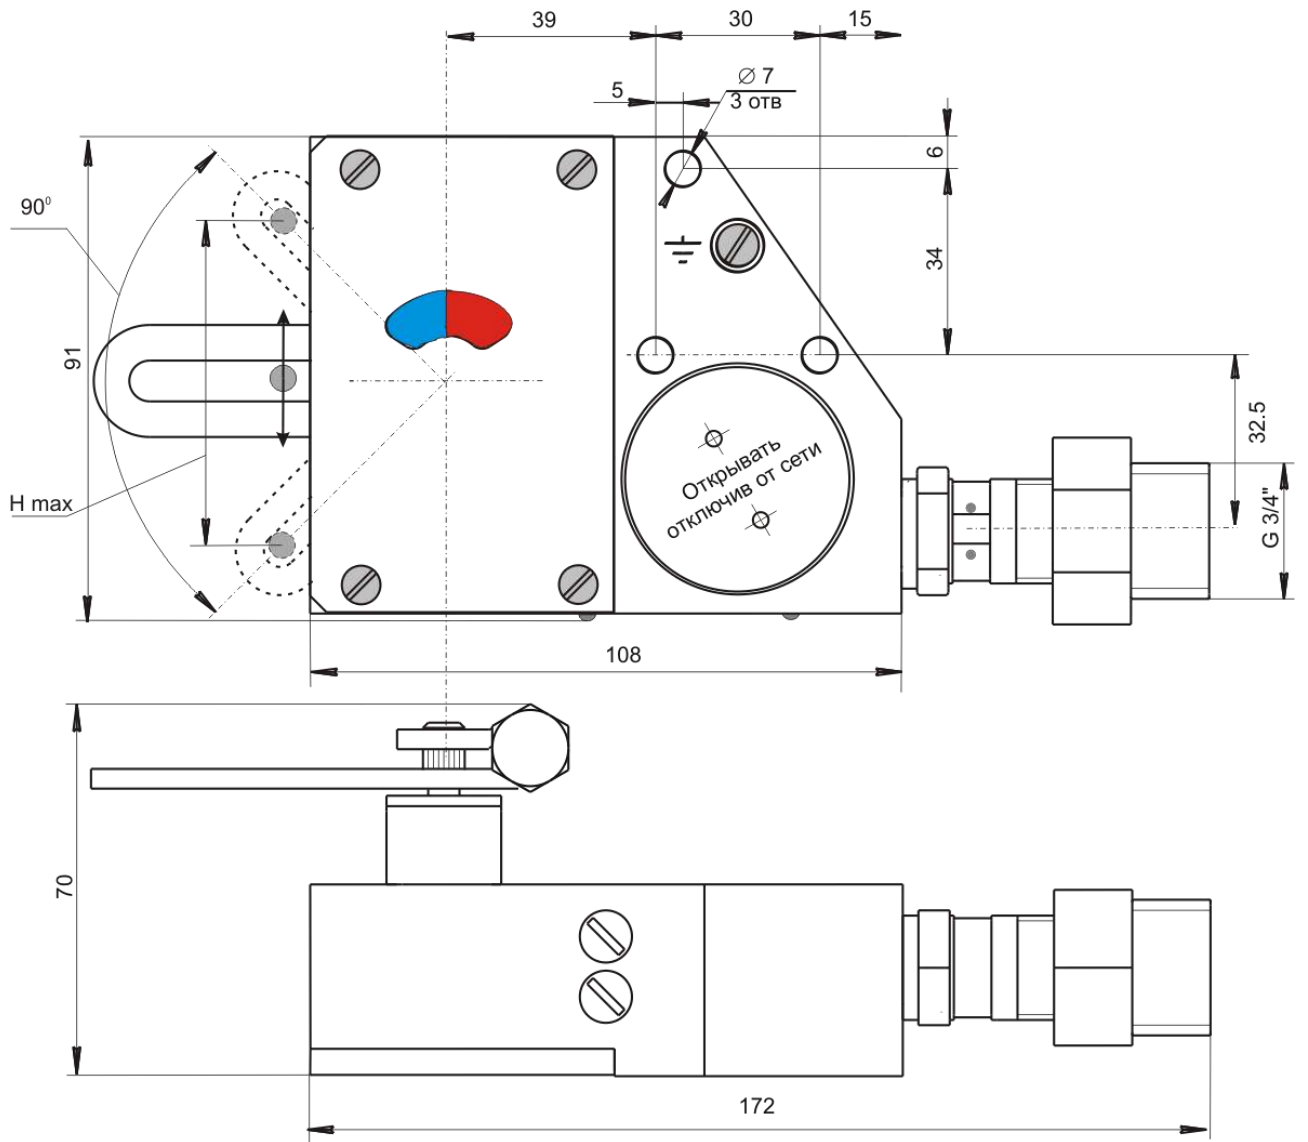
Монтажный чертеж выключателя KB-04
